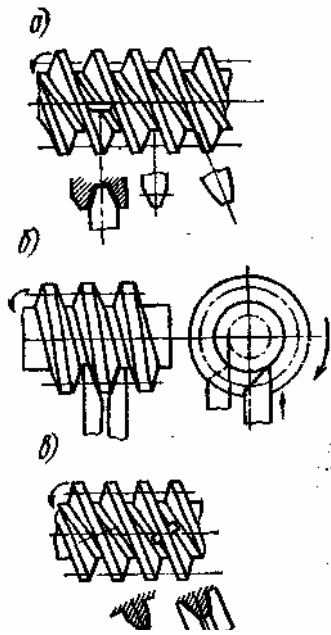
Виды цилиндрических червяков и схемы их обработки резцами:
